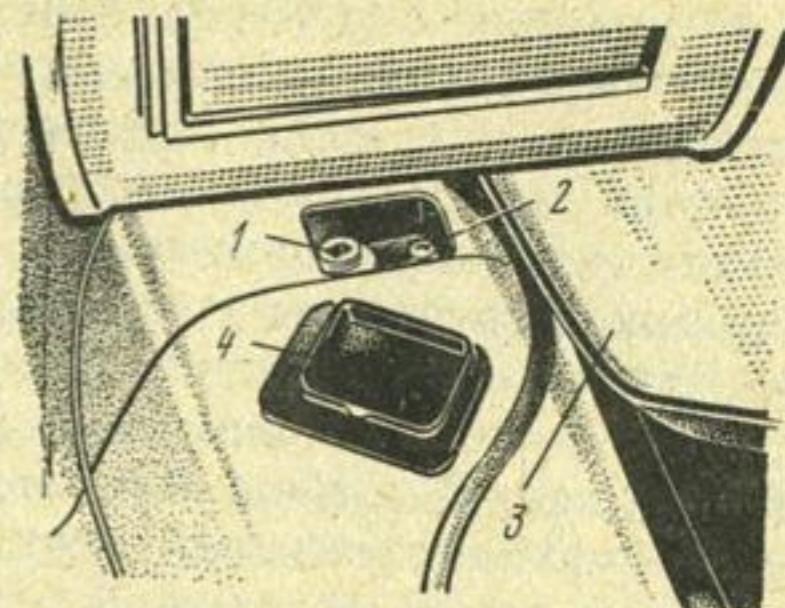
Расположение наливного отверстия и маслоизмерительного стержня в картере коробки передач
